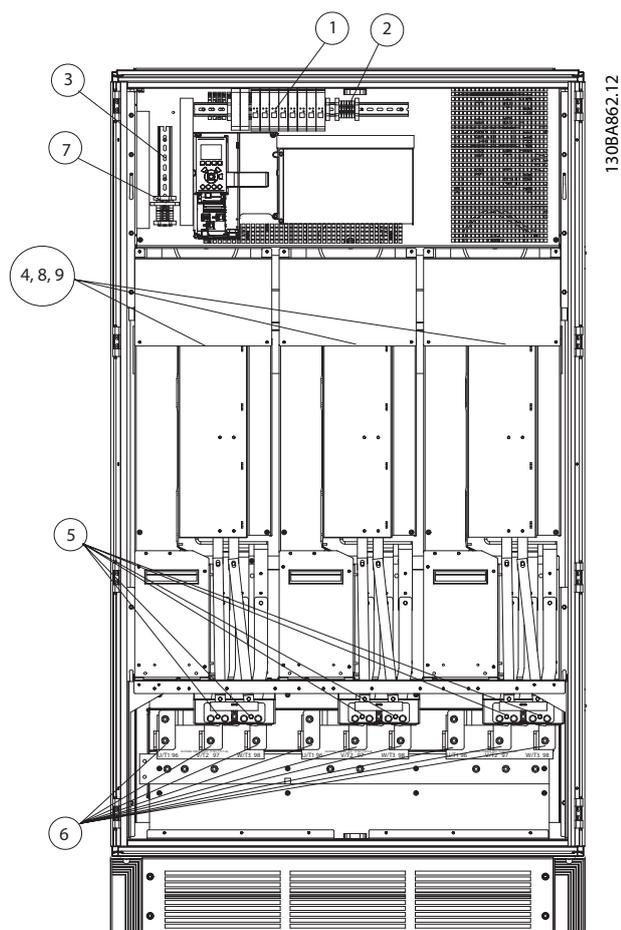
Шкаф инвертора, типоразмеры F12 и F13
